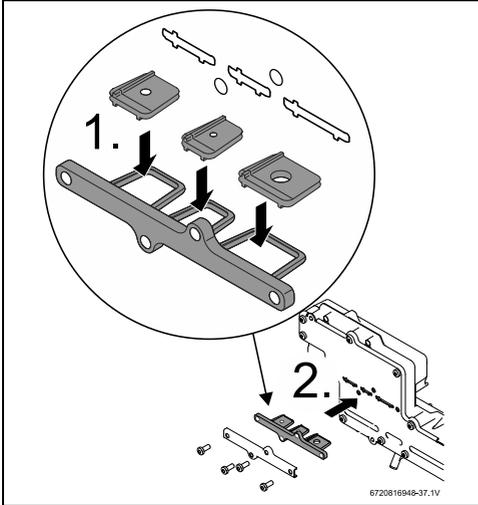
Assemblage de conversion de gaz pour l'appareil 199kBTU
